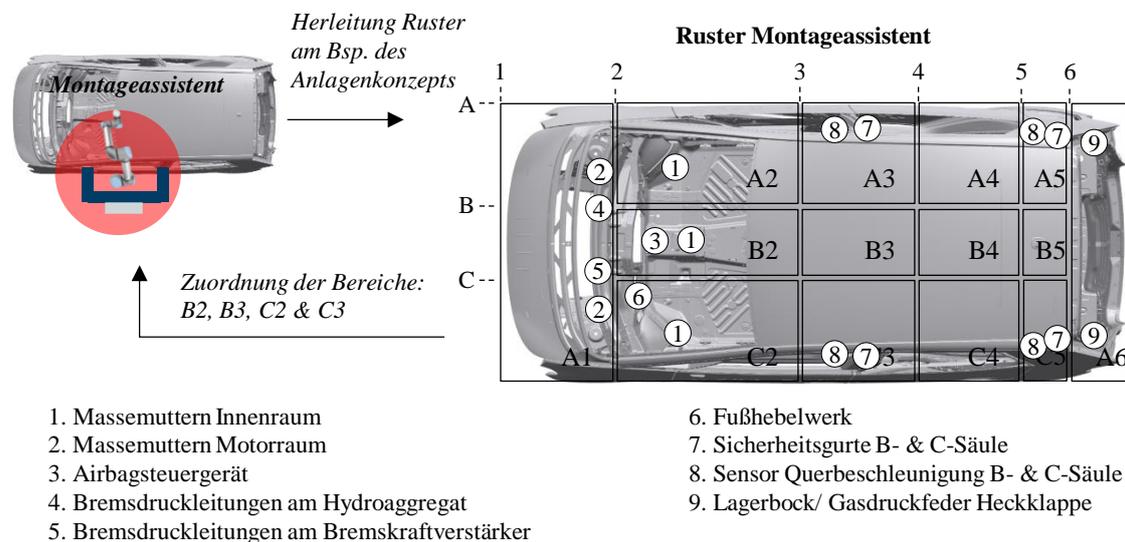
Ruster für die Schraubprozesse des Montageassistenten
